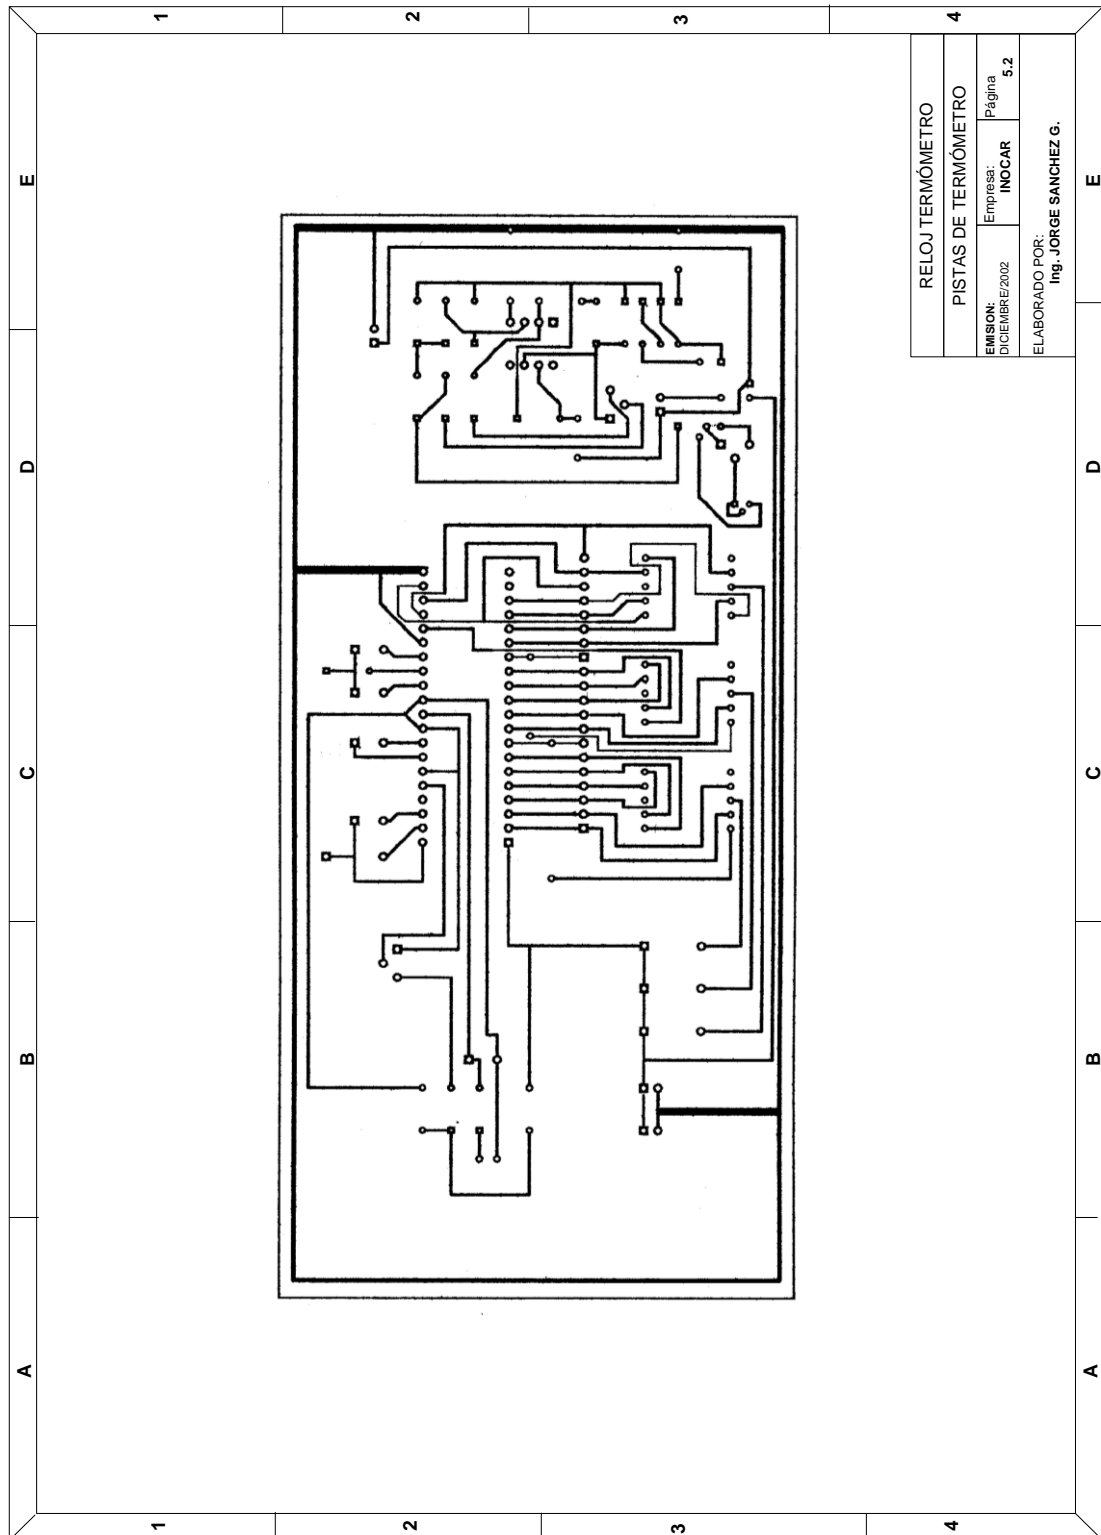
Tarjeta del termómetro (diagrama de pistas lado de soldadura)
